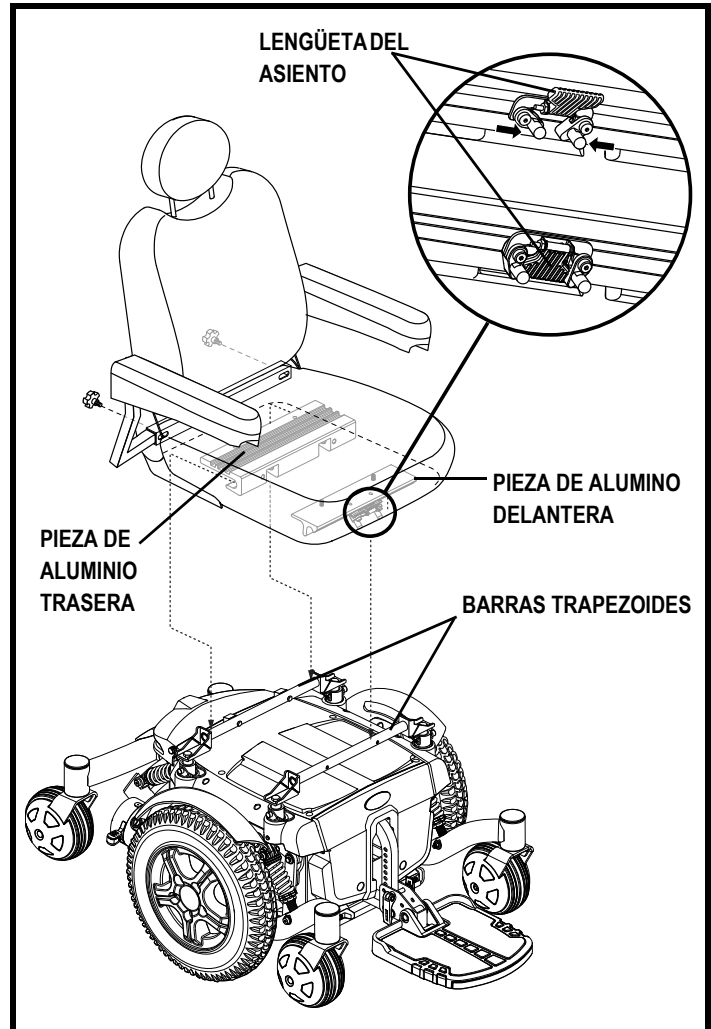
Sistema de Montaje Universal y el asiento contorneado
